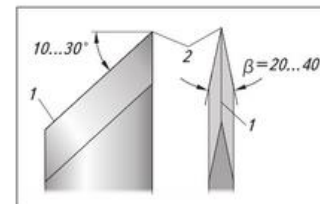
Лезвие косой токарной стамески: 1 – режущая кромка; 2 – вершина
